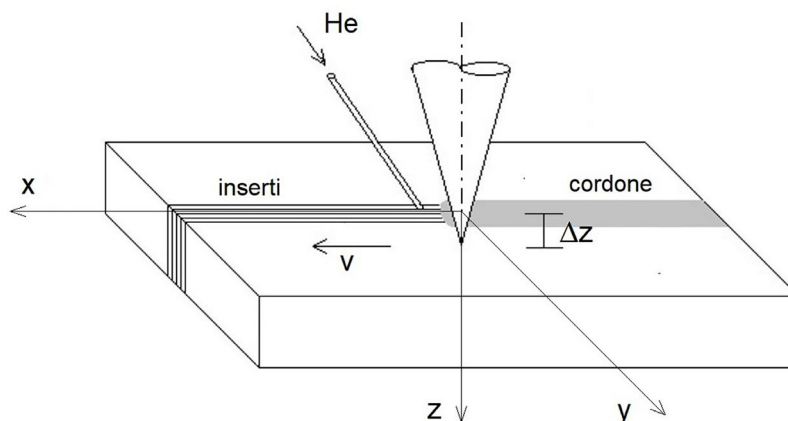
Schema del processo di saldatura / Scheme of the welding process
